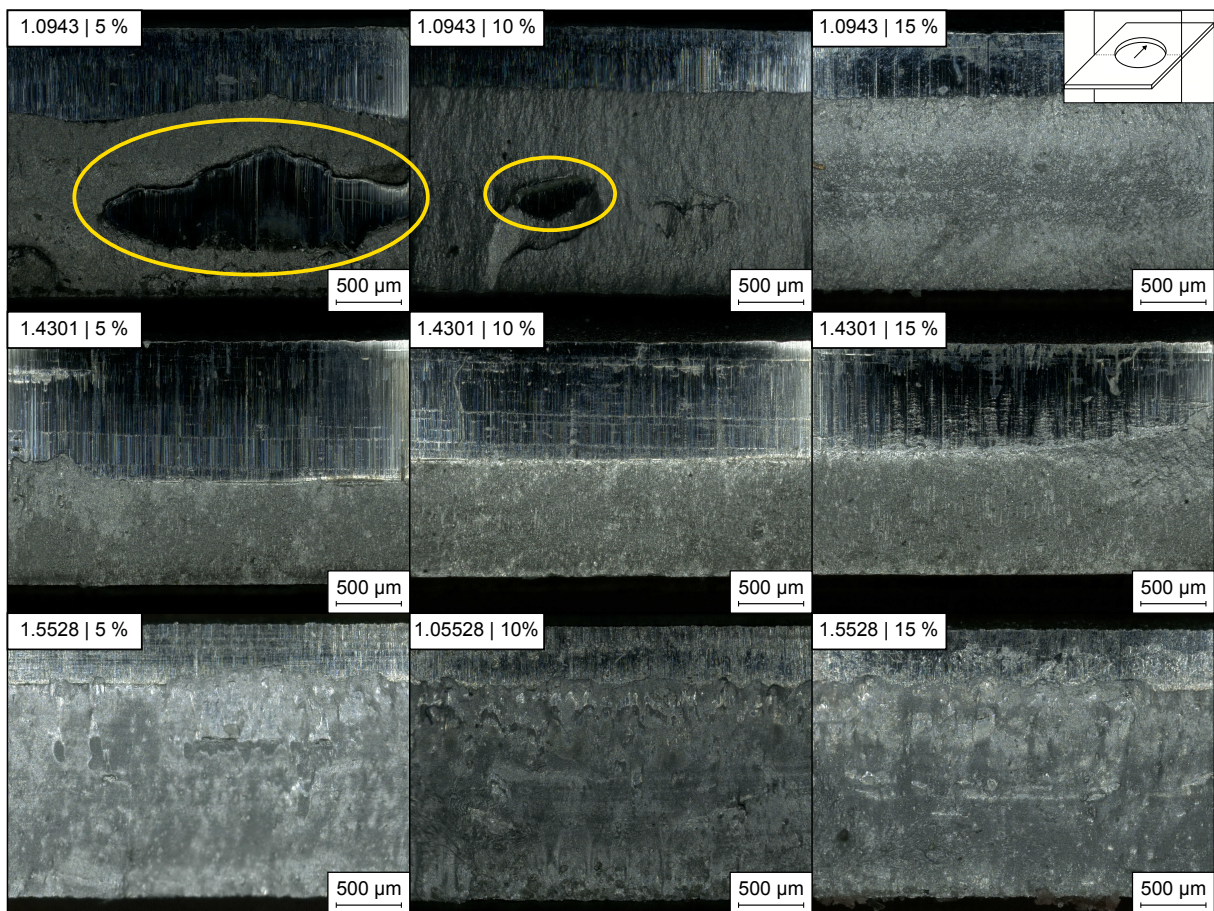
Frontalansichten der Schnittflächen für die Versuchsreihe Durchbruchkraft
